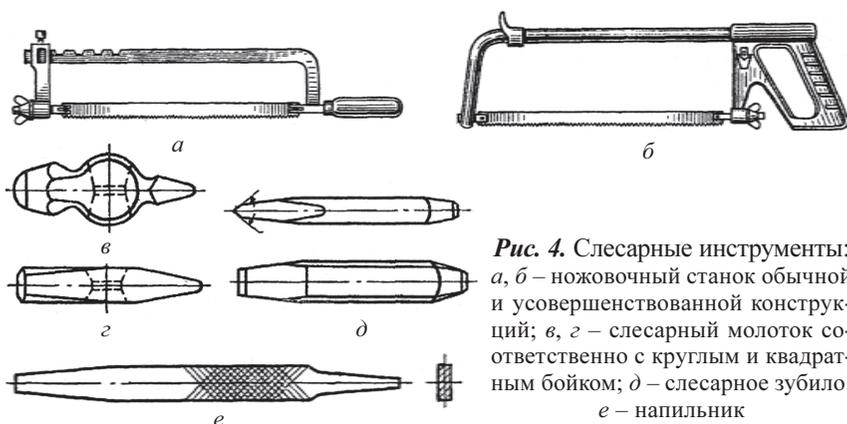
Слесарные инструменты: а, б – ножовочный станок обычной и усовершенствованной конструкций; в, з – слесарный молоток соответственно с круглым и квадратным бойком; д – слесарное зубило; е – напильник
